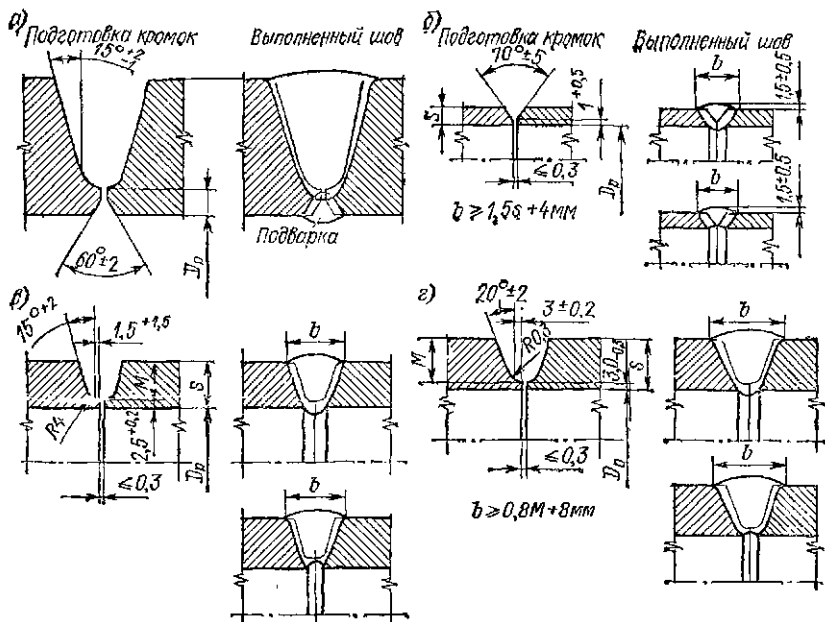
Типы разделки патрубков арматуры под сварку: а — С-12; б — С-23; в — С-29; г — С-42
